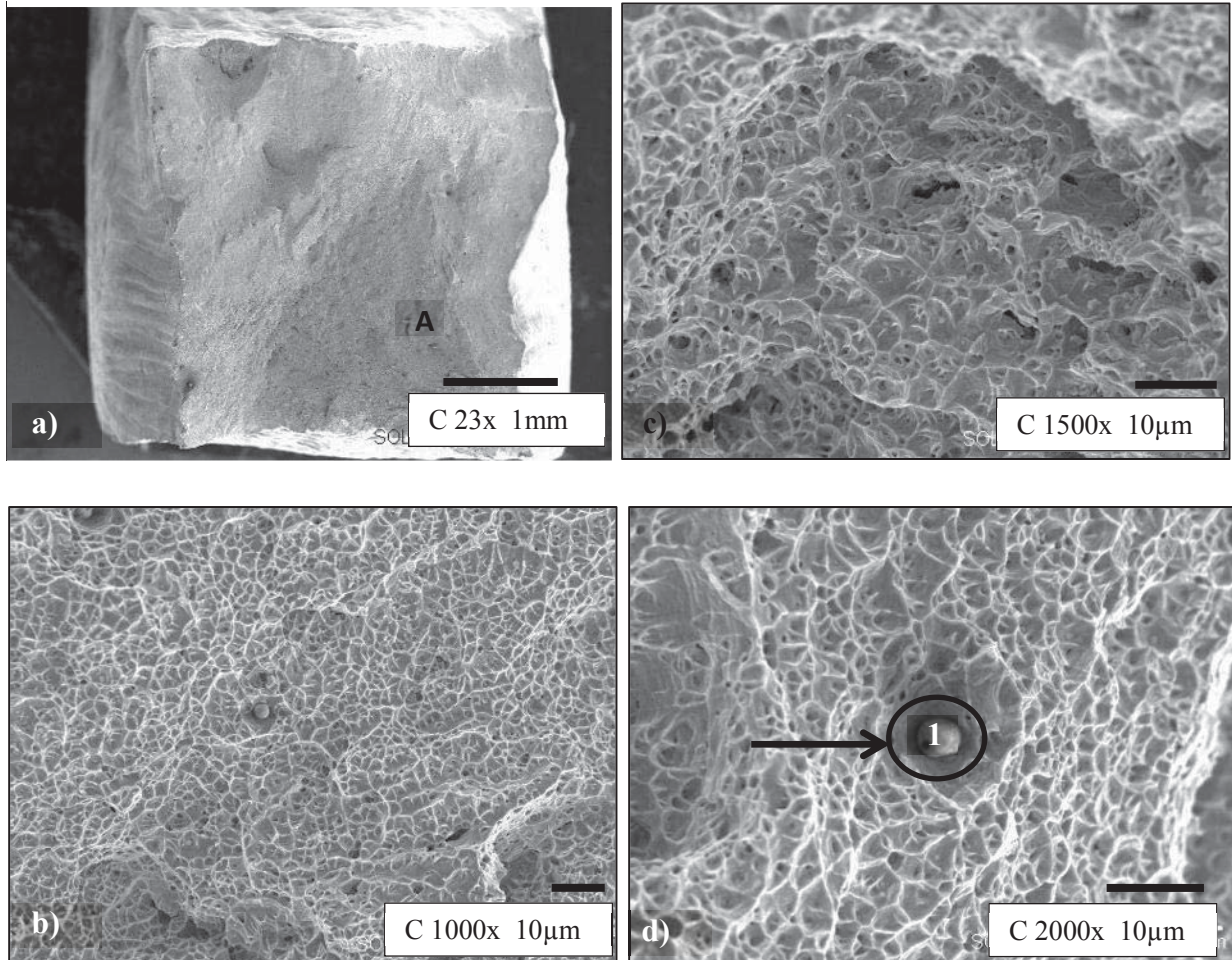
Imágenes de fractura de tensión en la unión soldada: a) Zona donde se realizó el estudio de fractura, b-c) detalles de fractura dúctil con presencia de microhuecos, d) Partícula encontrada en el interior de un microhueco.
